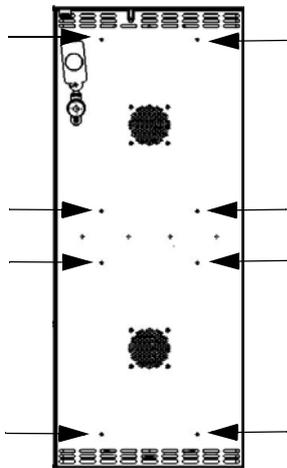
Entfernen des hinteren Luftleitblechs IMP 400
